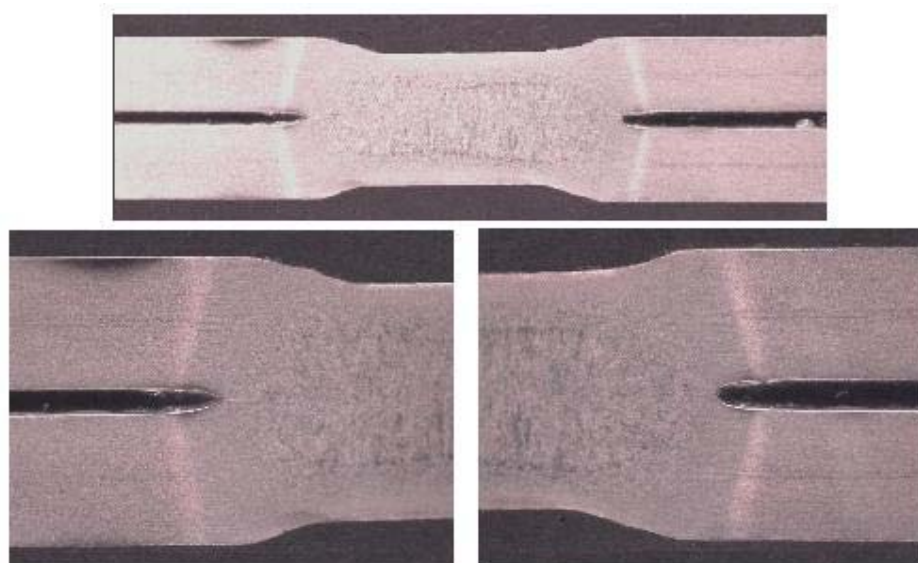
Entalhes gerados na lente de uma solda realizada no aço Dual-Phase 600 revestido soldada através do equipamento MFDC com eletrodos esféricos (espessura da chapa 1,19 mm).
